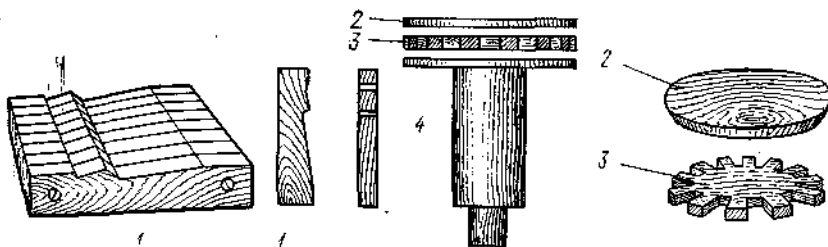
Изготовление шпиля: 1 — вельпсы; 2 — догмед; 3 — шпильгаты; 4 — шпindelь (веретено)
